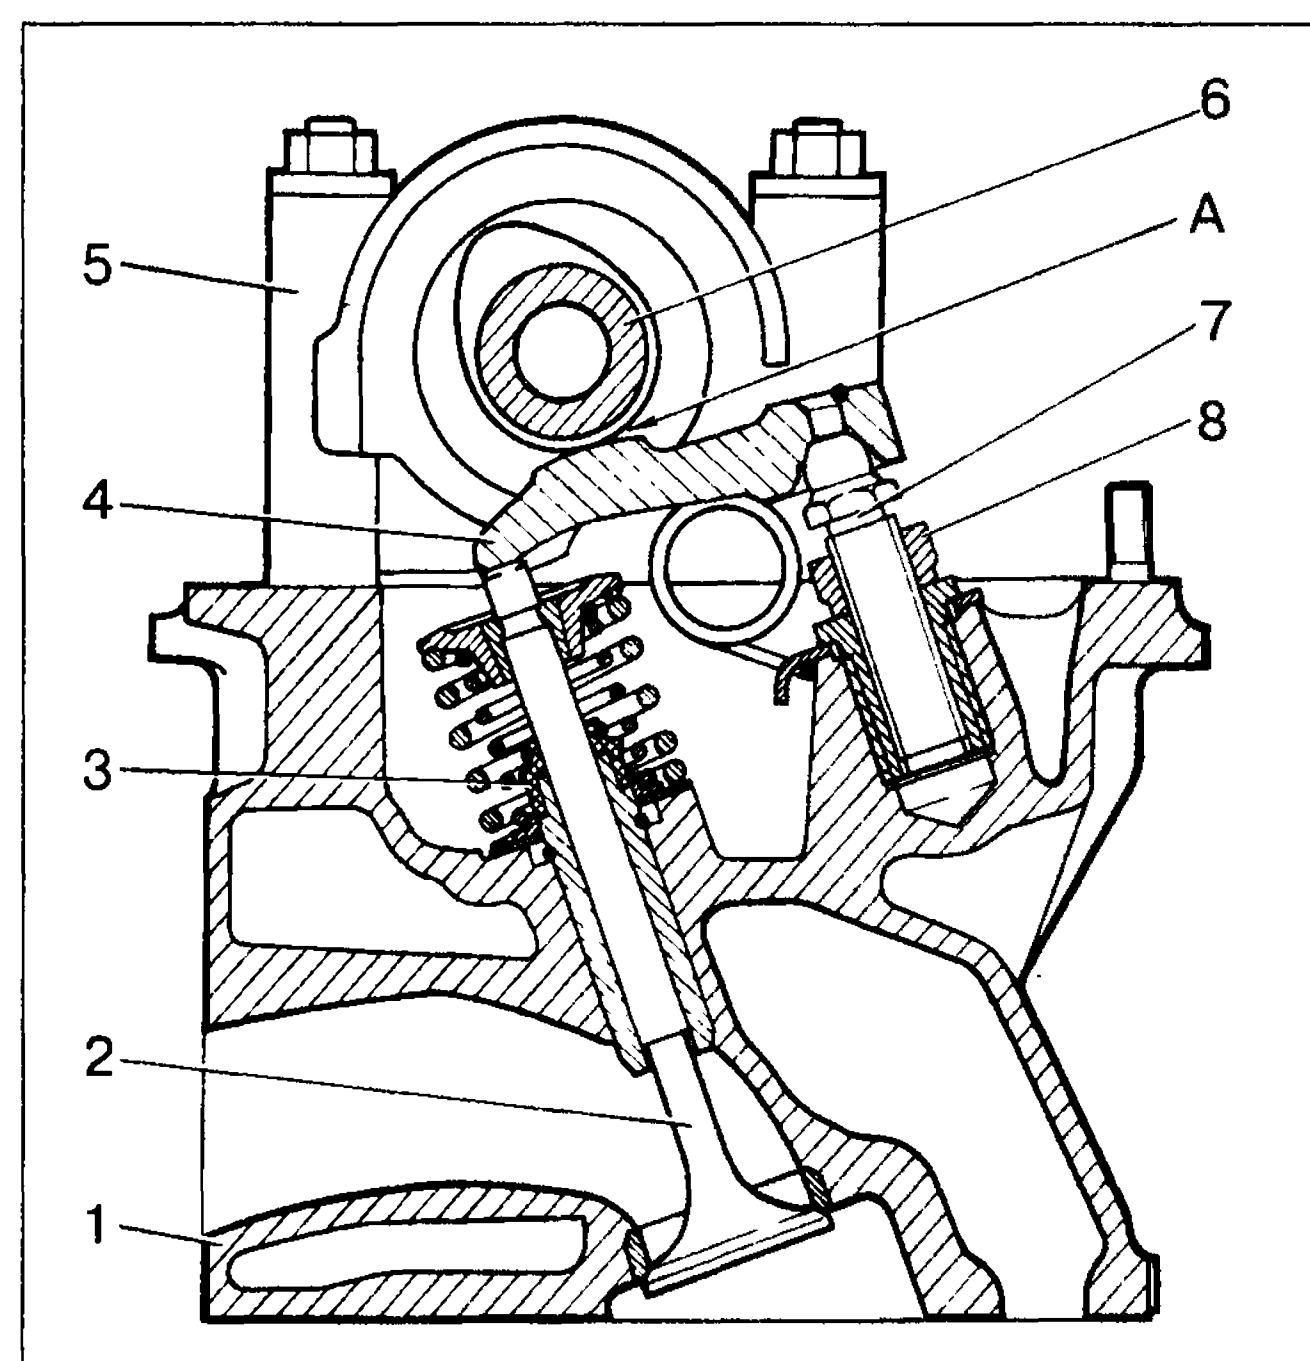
Разрез головки блока цилиндров по выпускному клапану: 1 - головка блока цилиндров; 2 - выпускной клапан; 3 - маслоотражательный колпачок; 4 - рычаг клапана; 5 - корпус подшипников распределительного вала; 6 - распределительный вал; 7 - регулировочный болт; 8 - контргайка болта; А - зазор между рычагом и кулачком распределительного вала
